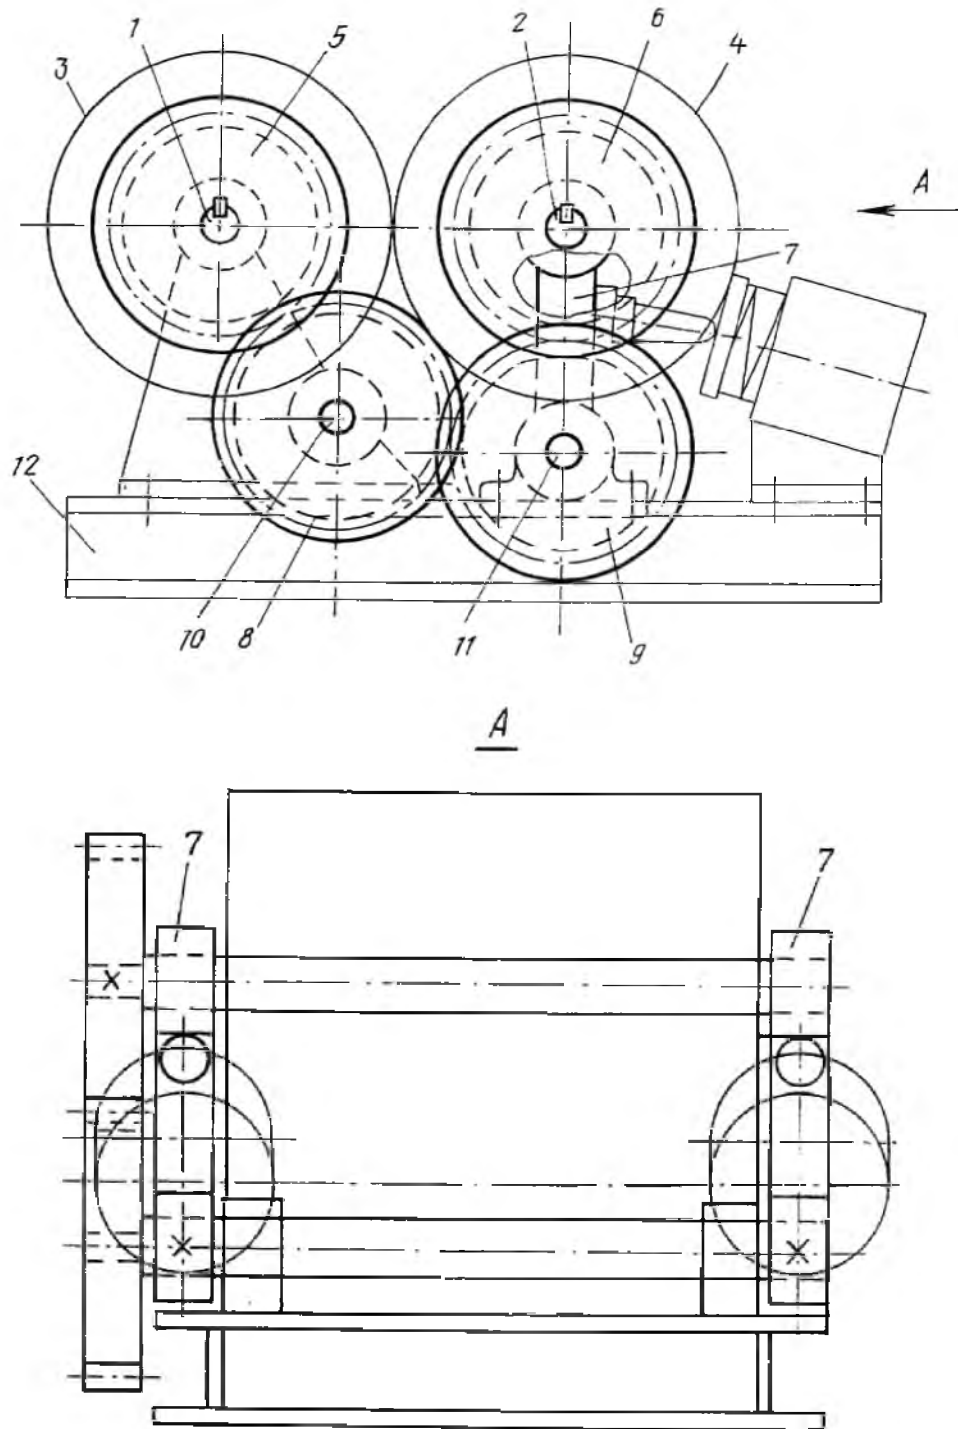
Конструкція передавального механізму валкової дробарки
